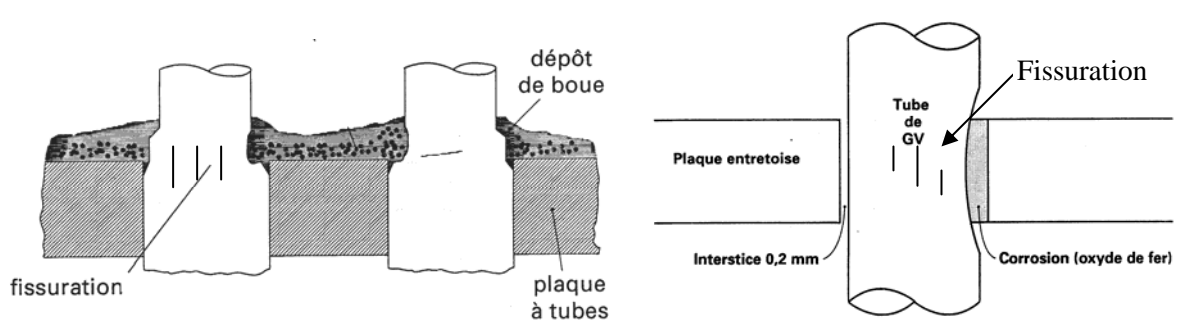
Fissuration au niveau de la plaque à tubes et de la plaque d'entretoise.
